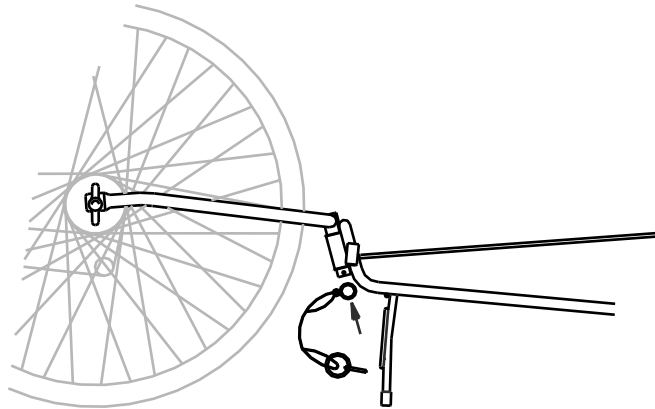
Insertion de l'anneau soudé et de l'esse
